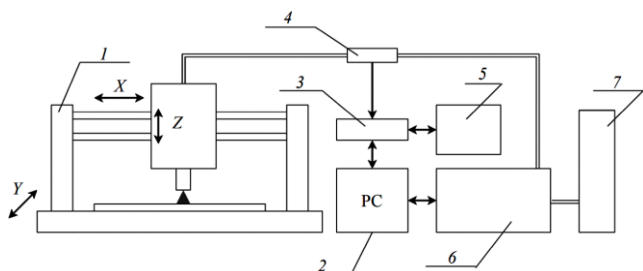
Экспериментальный стенд по 3D-наплавке на базе станка с ЧПУ: 1 – 3-координатный станок с ЧПУ портального типа; 2 – ПК; 3 – АЦП/ЦАП; 4 – датчики силы тока и напряжения; 5 – система ЧПУ; 6 – сварочный полуавтомат; 7 – баллоны с защитным газом
